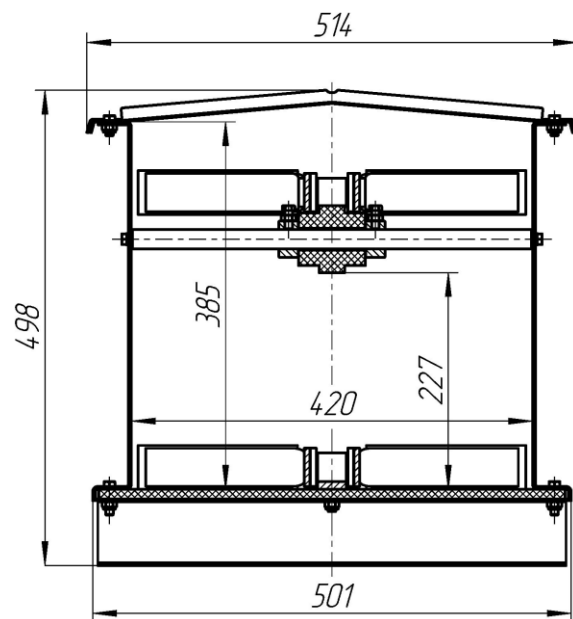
Станция натяжная ТСЦ-100. Размеры габаритные
